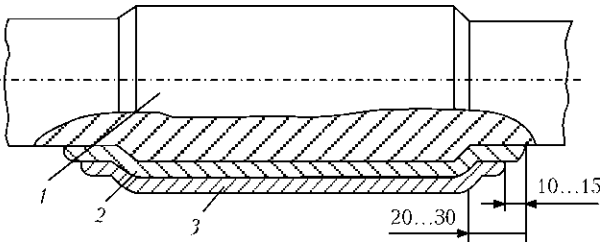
Схема выполнения антикоррозионной наплавки вала: 1 — основной металл; 2 — низкоуглеродистый металл наплавленного подслоя; 3 — высоколегированный аустенитный наплавленный металл
